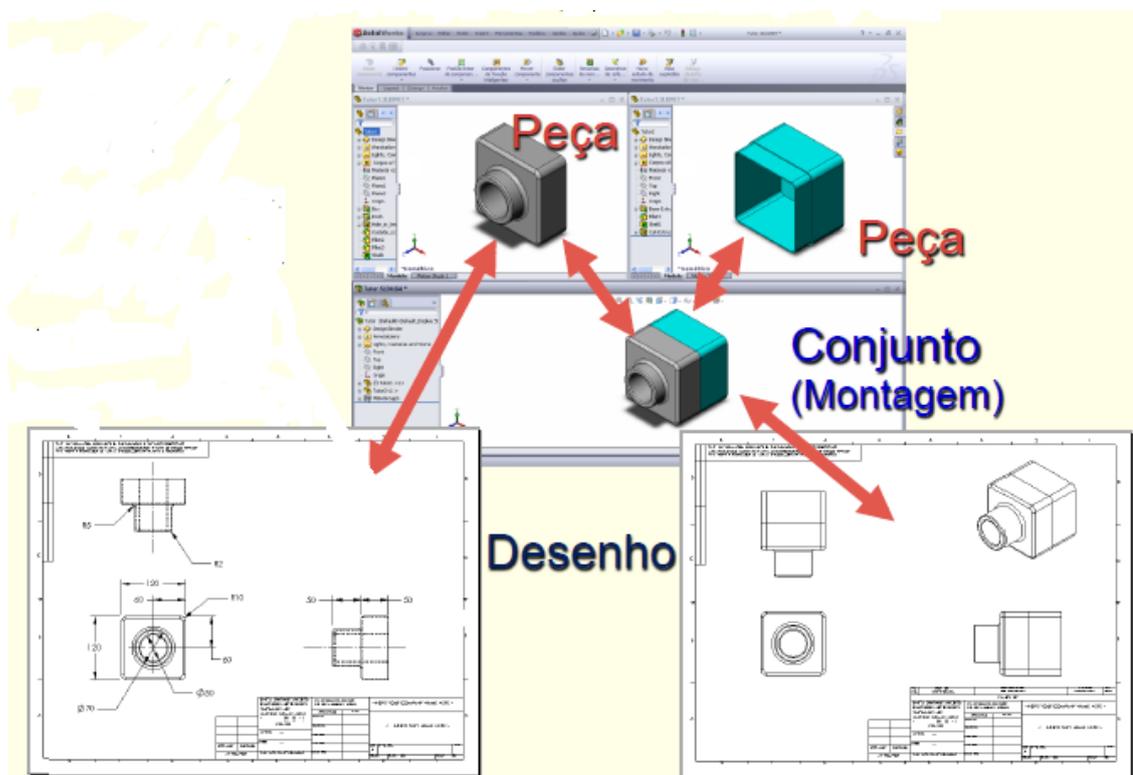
Modelo do *SolidWorks* constituído por componentes (*parts*), conjuntos (*assembly*) e desenhos (vistas, *drawing*).
